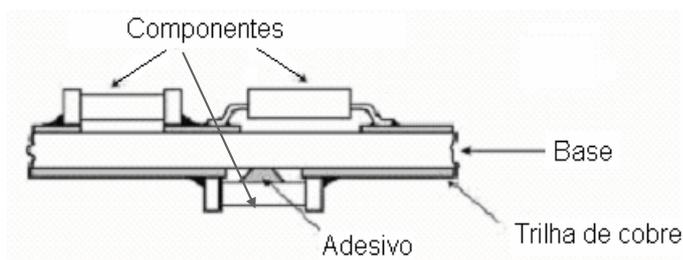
Montagem de componente utilizando a tecnologia SMT [4]
